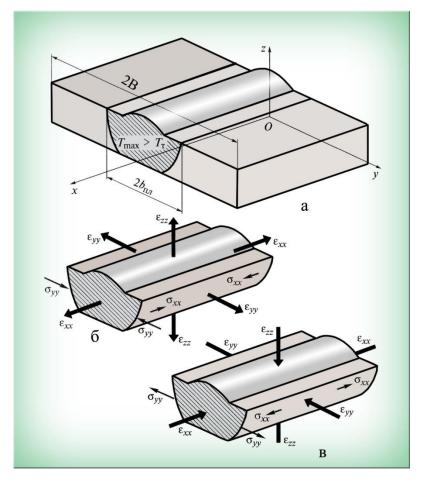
Схема образования сварочных деформаций и напряжений при сварке пластин в стык: а – активная и пассивная зоны; б, в – деформации и напряжения в активной зоне на стадиях нагрева и охлаждения
